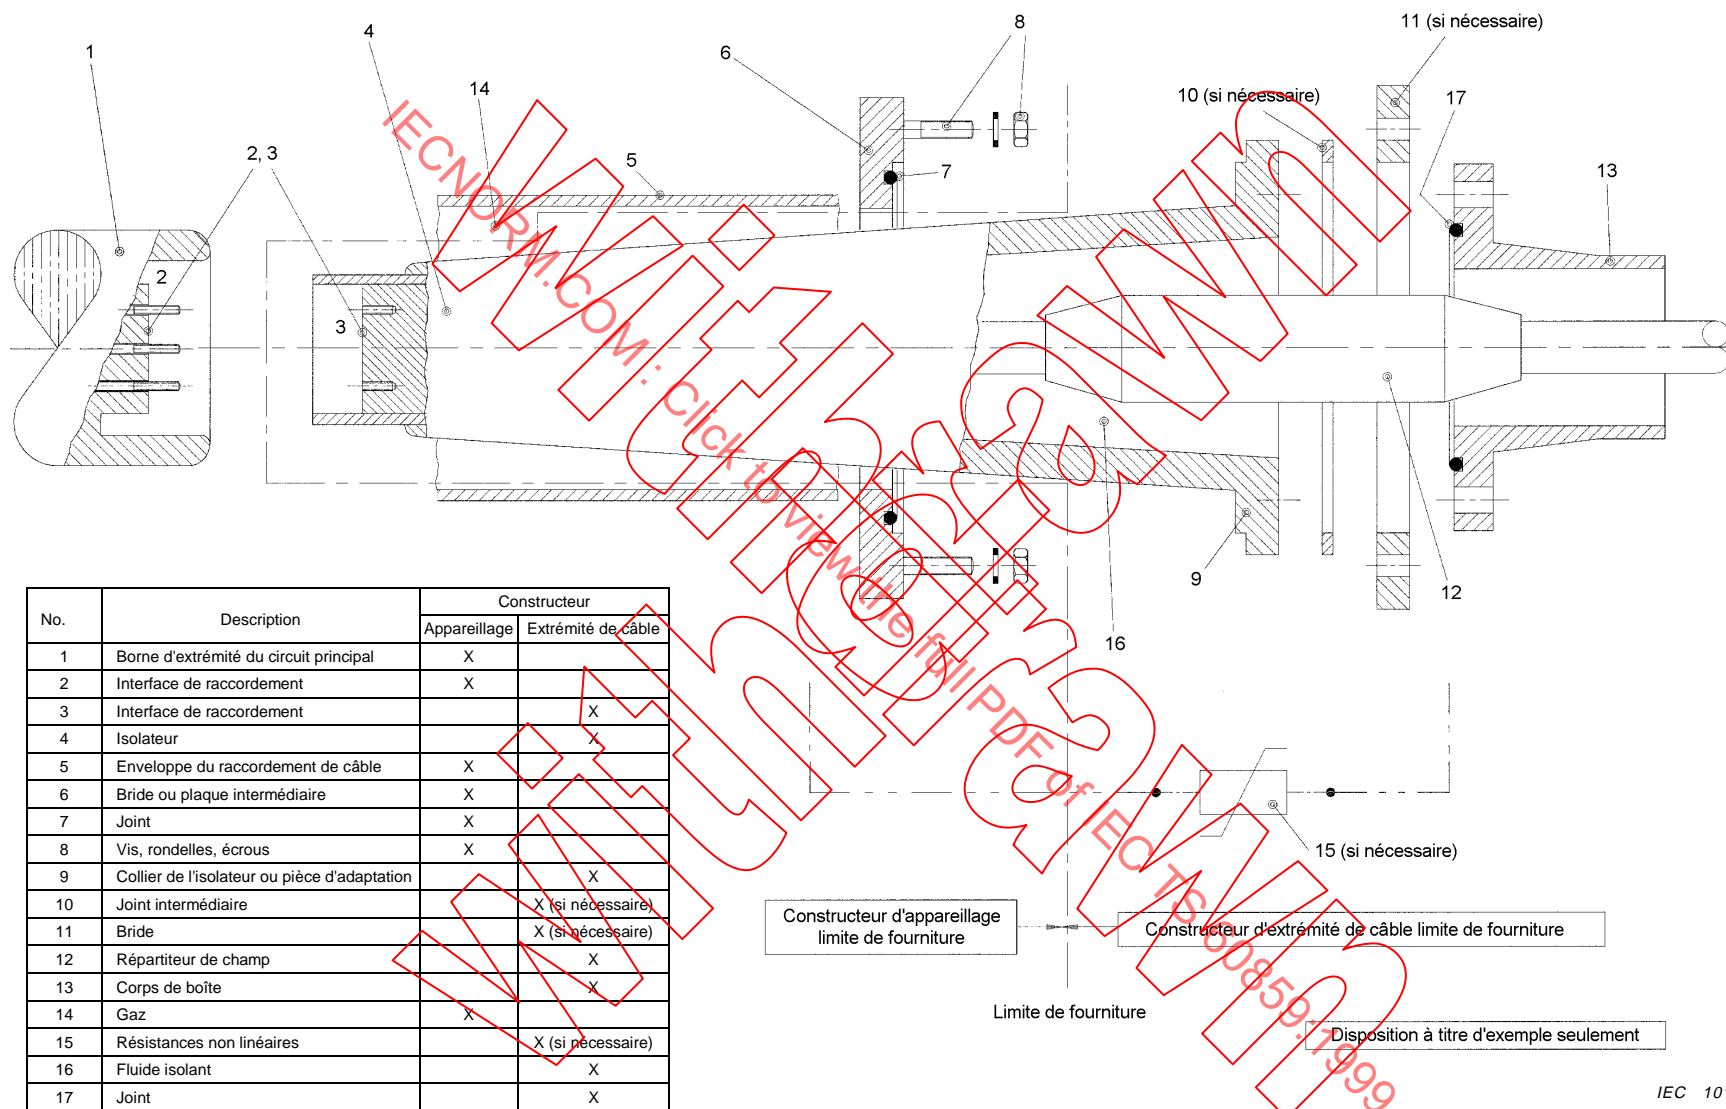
Assemblage de raccordement de câble rempli d'un fluide – Exemple de disposition
